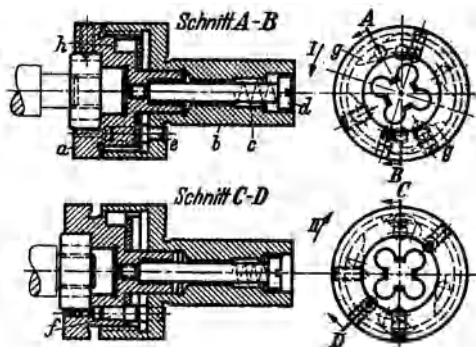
Halter für Gewindeschneidwerkzeuge.
